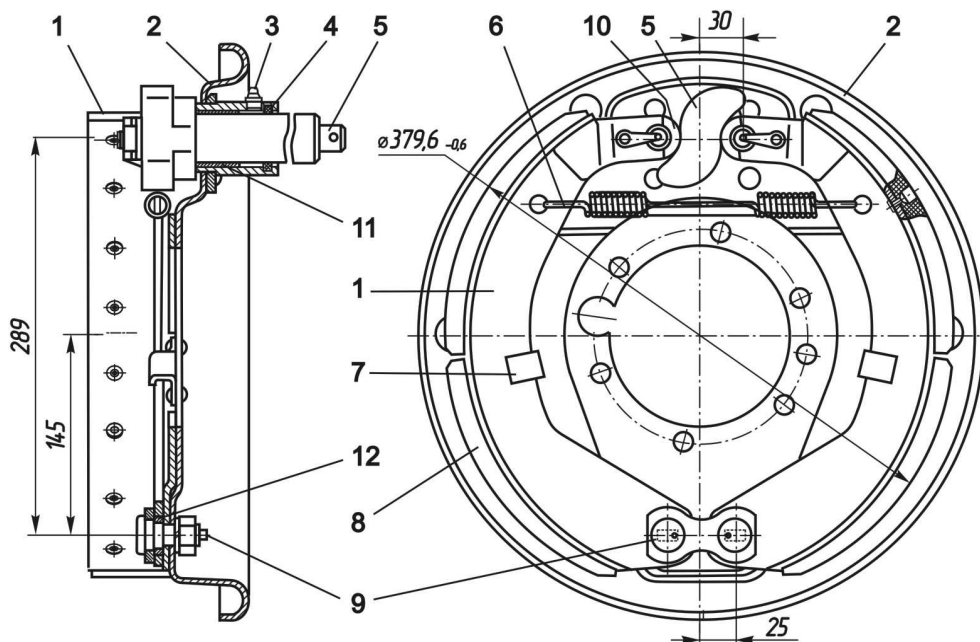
Тормозной механизм автобуса ПАЗ-32053 ("КААЗ")
